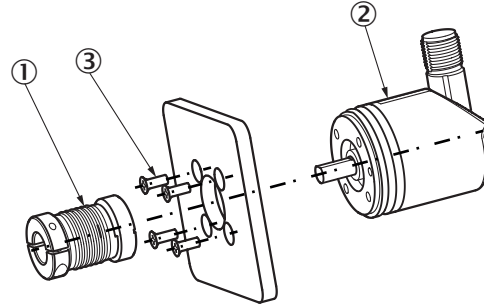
Anbau über flanschseitige Gewindebohrungen
